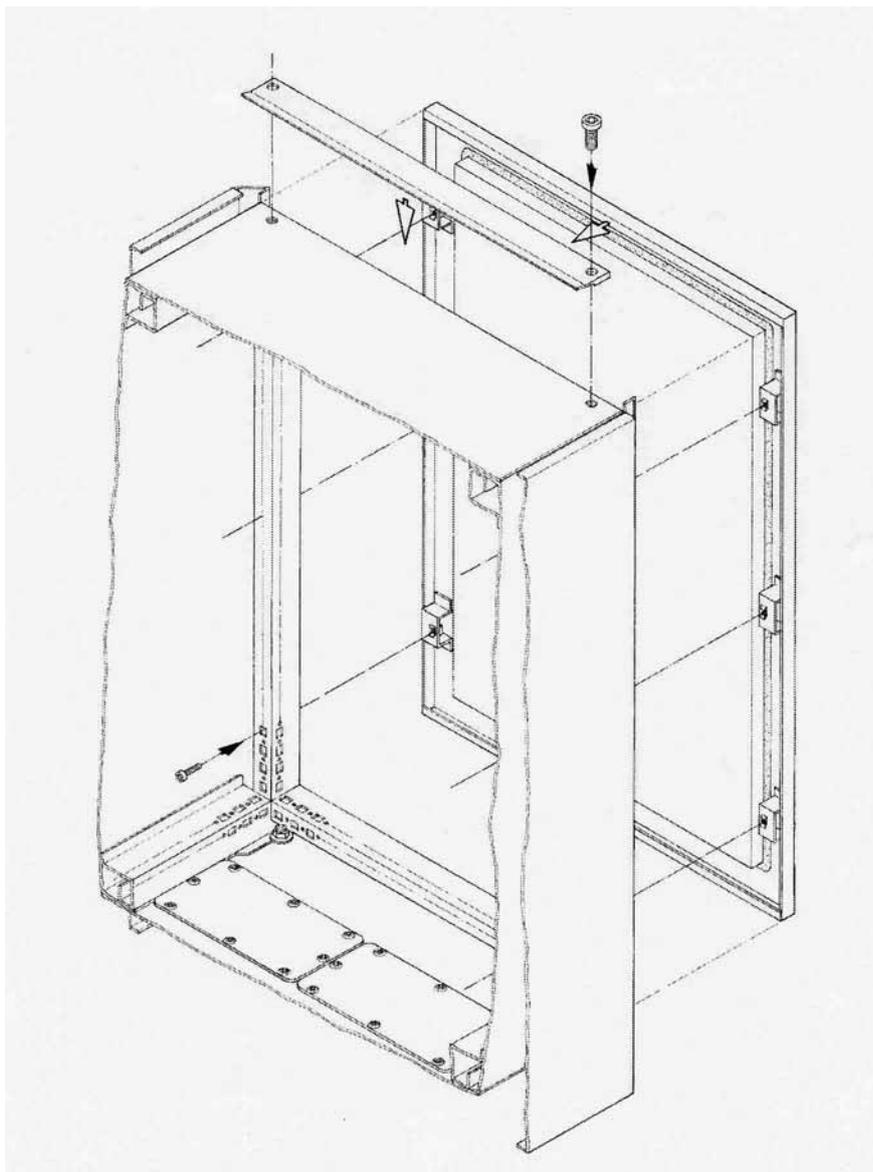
Монтаж/демонтаж внутренней стенки задней стенки
